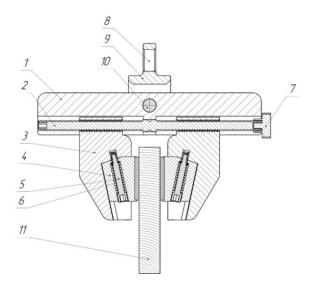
Общий вид фрикционного ГЗУ с клиновыми КЭ: 1 – корпус; 2 – зажимной винт; 3 – ползун; 4 – клиновый контактный элемент; 5 – крепежный винт; 6 – возвратная пружина; 7 – маховичок; 8 – проушина; 9 – скоба; 10 – ось; 11 – изделие из древесины
